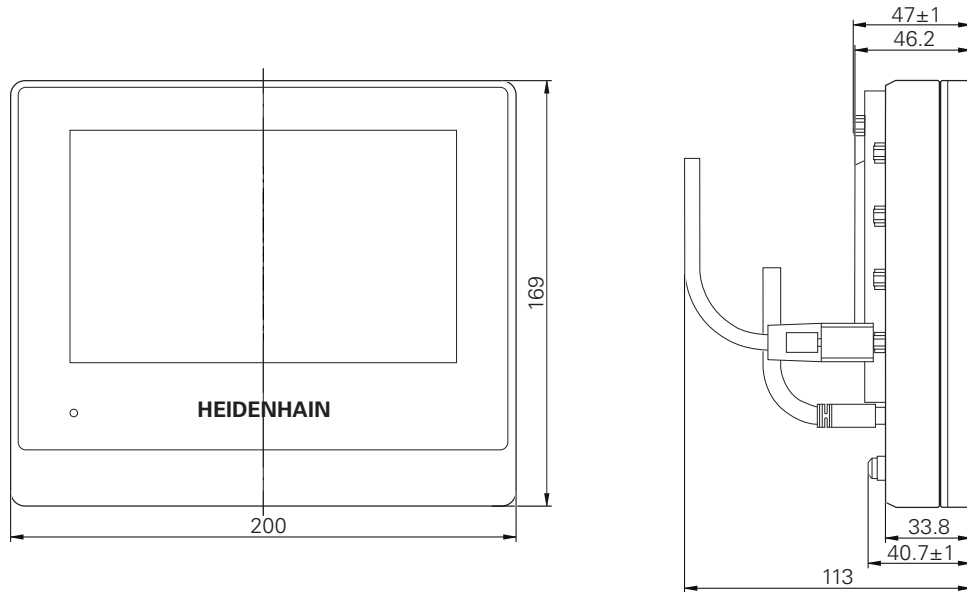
Dimensioner för enhetens hölje med ID 1089179-xx
